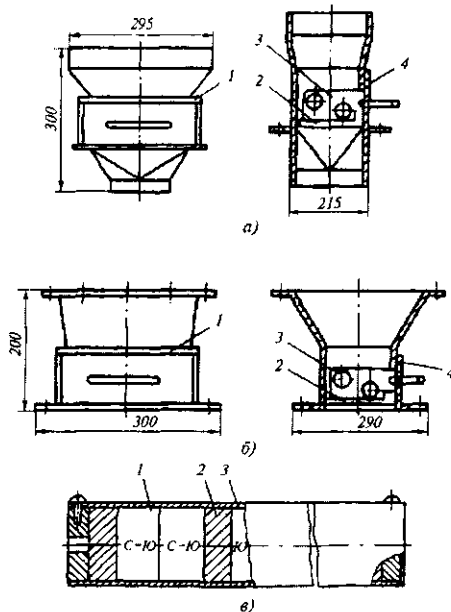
Магнитный сепаратор: а - У1-БМЗ; б - У1-БМЗ-01; в - цилиндрический магнит
